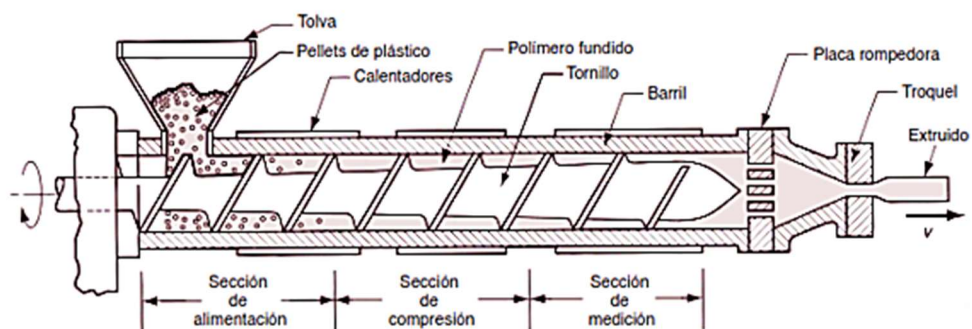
Esquema extrusor de un solo tornillo [17]
